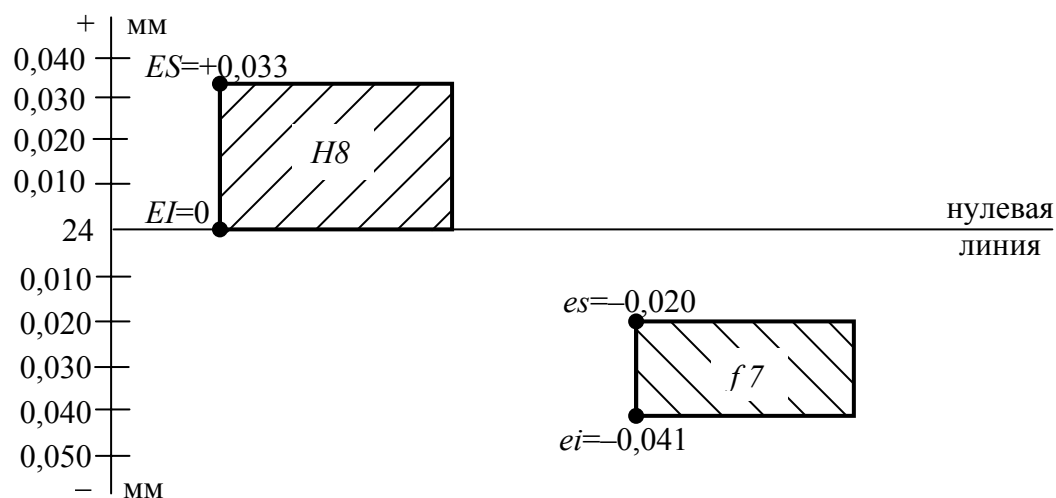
Схема расположения полей допусков деталей
